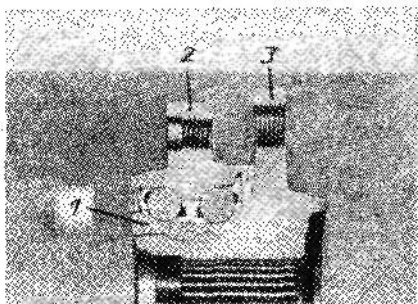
Двухрядный радиально-упорный шариковый подшипник третьего поколения, предназначенный для ведущего переднего колеса. Внутреннее кольцо выполнено составным (детали 1 и 3) со смещением разъема влево для возможности полного заполнения узла шариками и повышения за счет этого его грузоподъемности. Наружное кольцо 2 соединяется болтами с опорой подшипника колеса. Подшипник снабжен долговечным смазочным материалом. Кромки уплотнительных колец скользят по внутреннему и наружному кольцам
